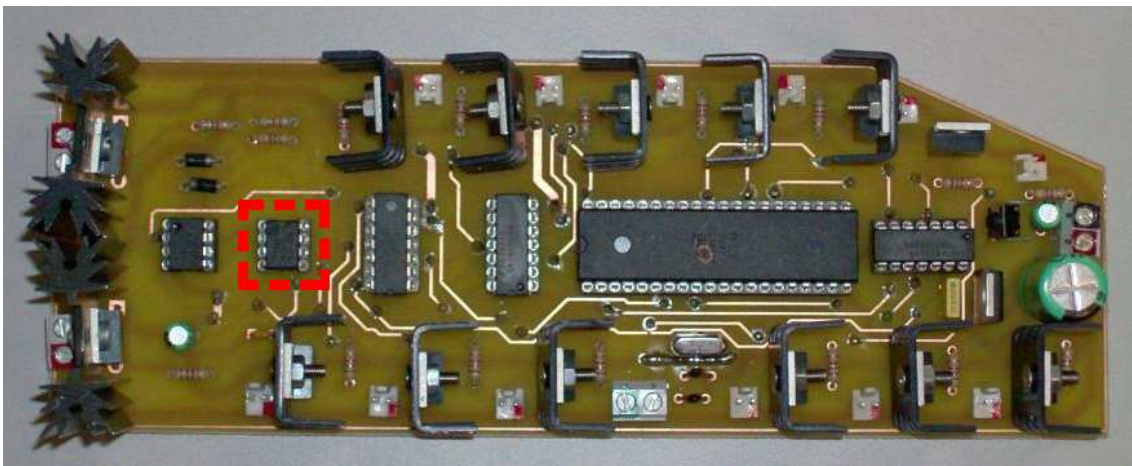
Disposición del integrado LM555 en la placa PCB, encuadrado en rojo.
